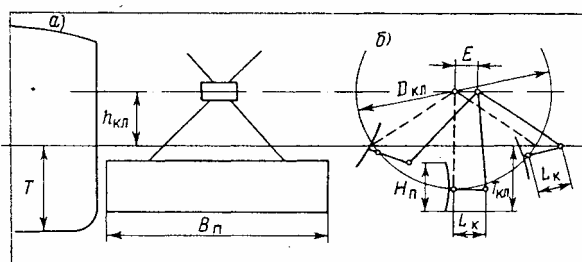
Схема гребного колеса с поворотными плицами: а - вид с носа; б — вид сбоку
